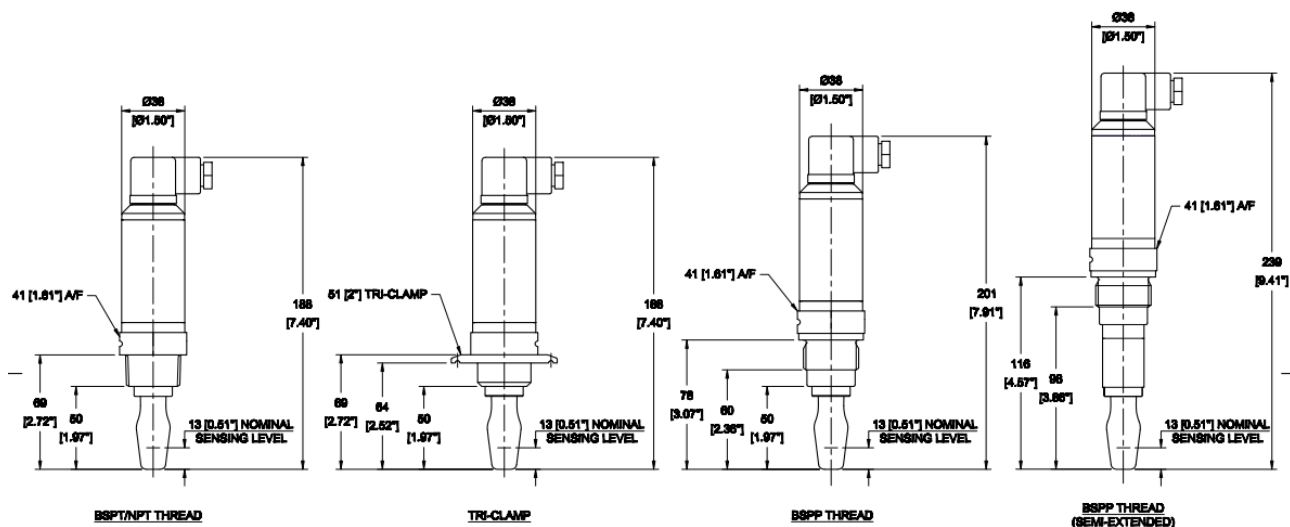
6 Зовнішній вигляд та габаритні розміри Rosemount 2110
